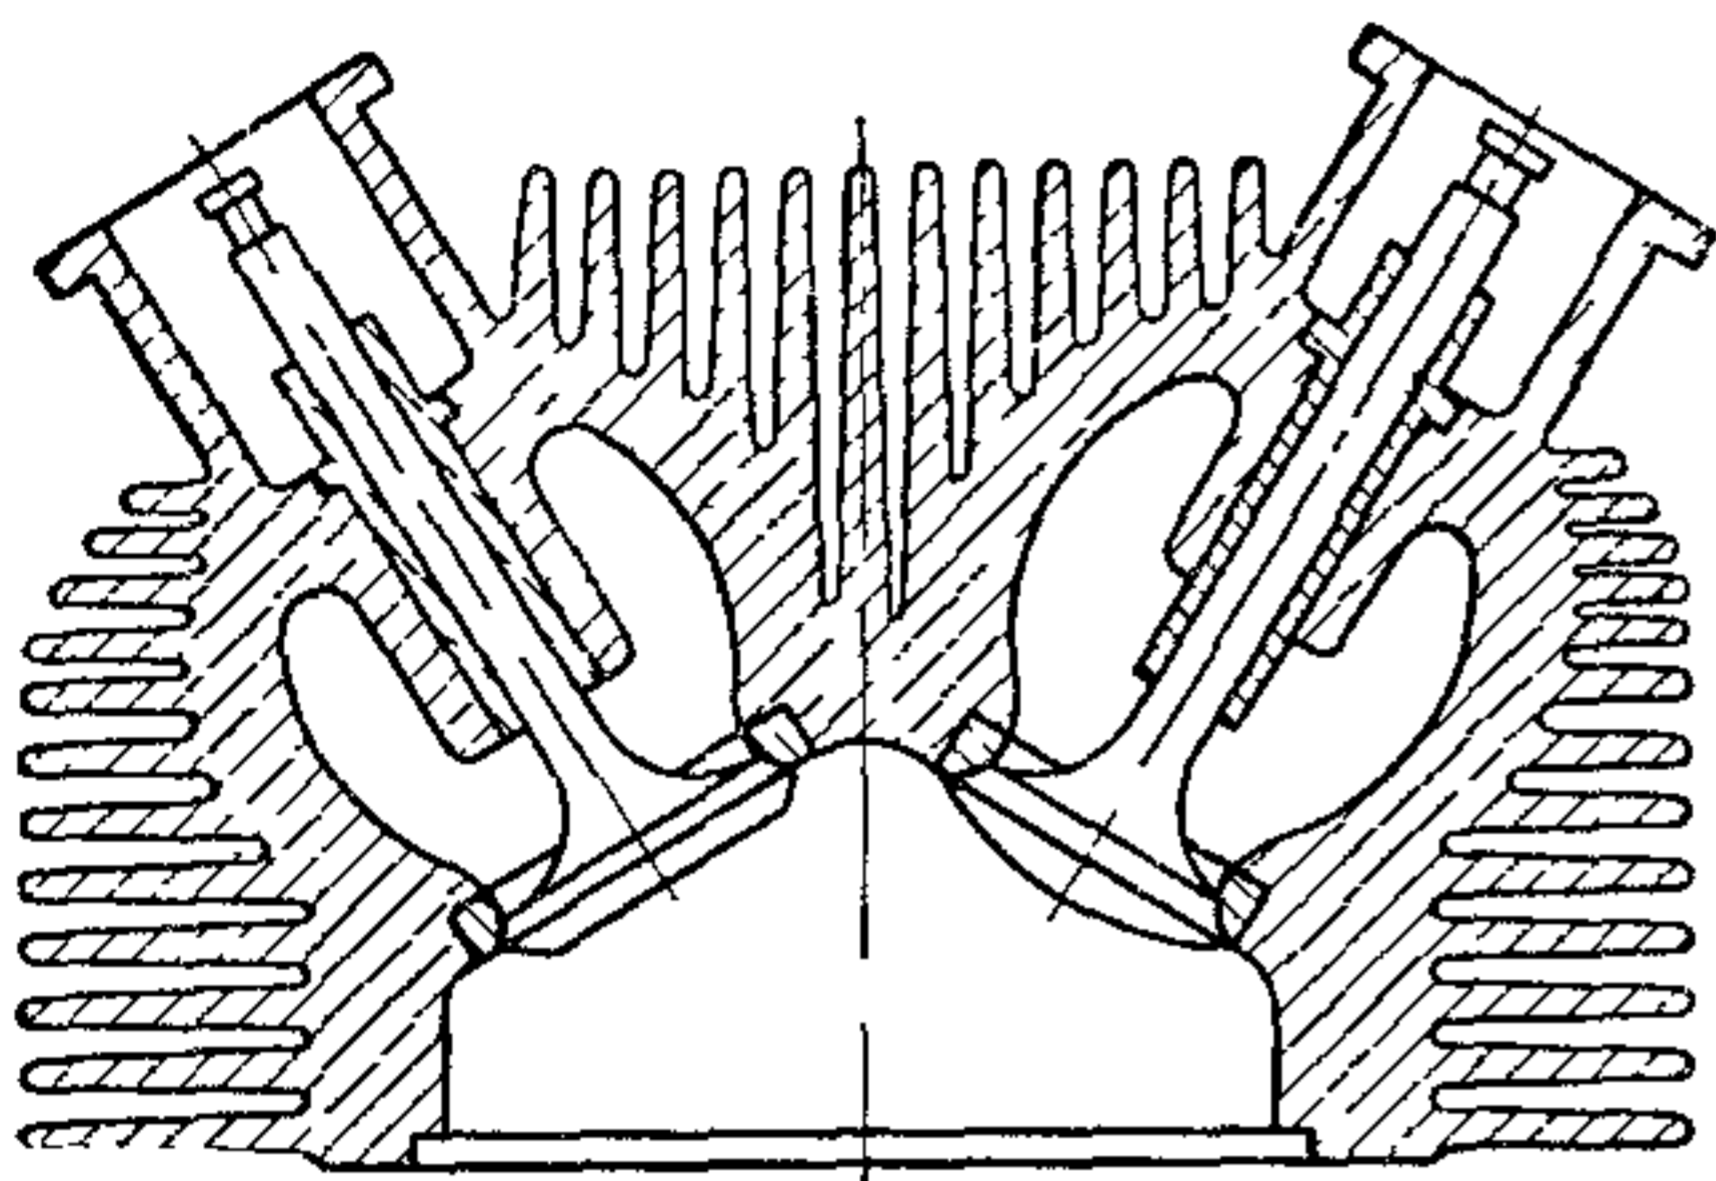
Головка цилиндров двигателя с воздушным охлаждением
